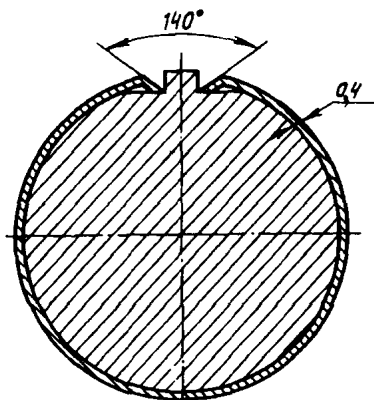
Схема установки упругой ДРД на шейку вала
